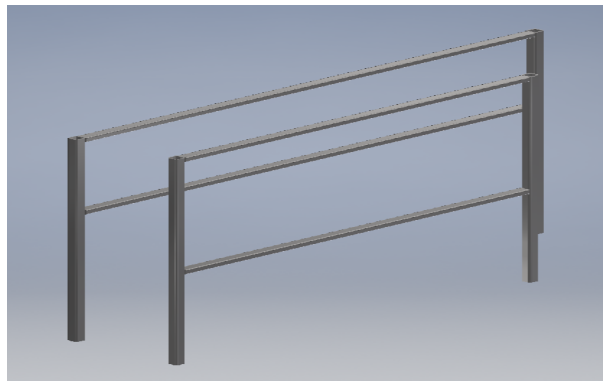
Modelo CAD de columnas de la banda transportadora de perfiles transversales.
